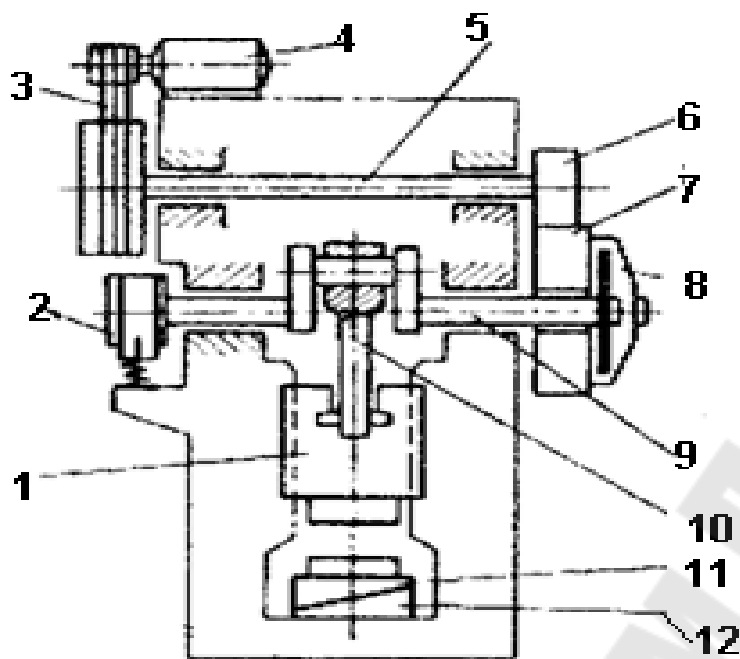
Кинематическая схема кривошипного пресса: 1 -- ползун; 2 - тормоз; 3 - клиноремная передача, электродвигатель; 5 - промежуточный вал; 6 - шестерня; 7 - зубчатое колесо; 8 - дисковая муфта; 9 - кривошипный вал; 10 - шатун; 11 - стол пресса; 12 - клин
